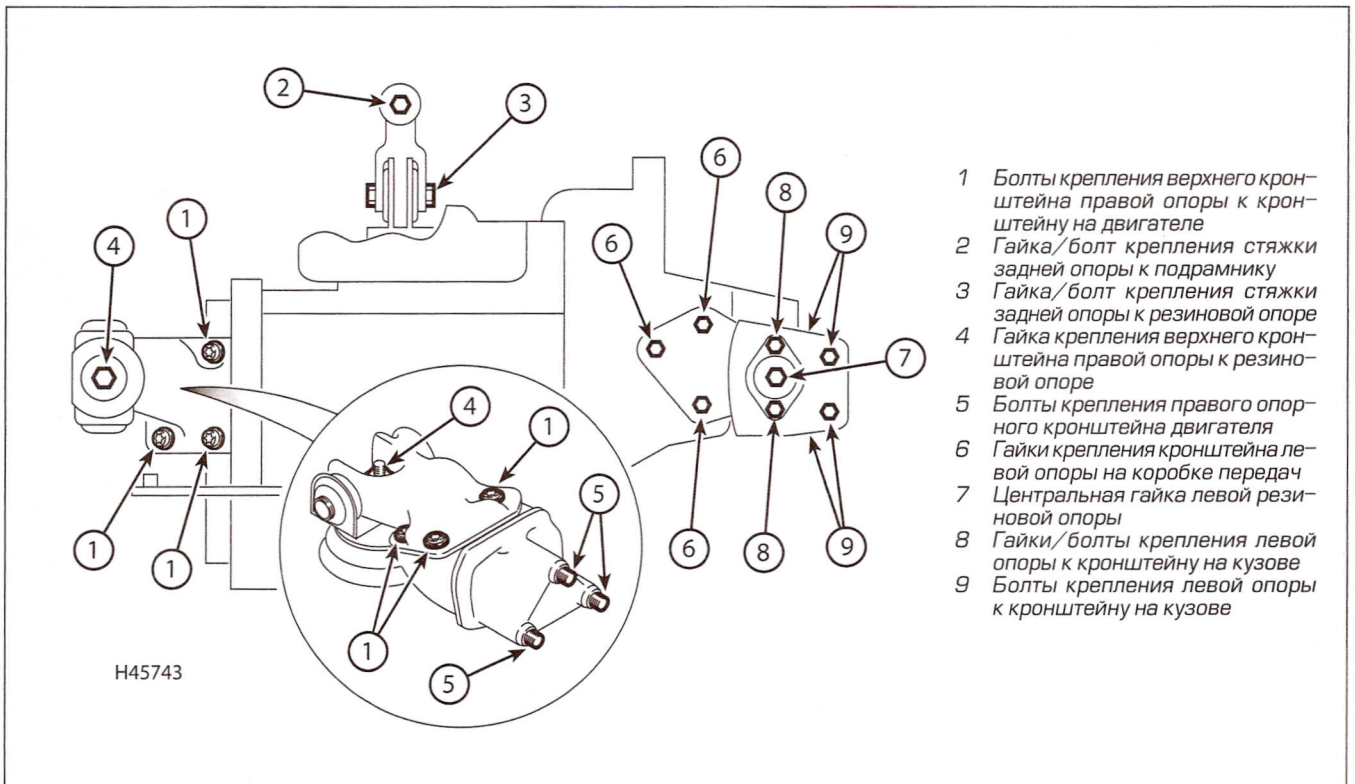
, б. Элементы и болты/гайки крепления опор двигателя/коробки передач (двигатели 1.6 л)
